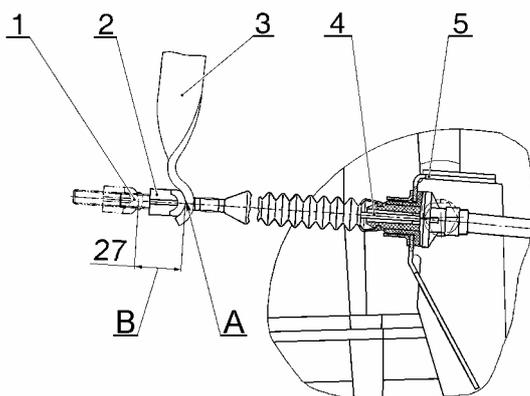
Механизм привода сцепления автомобиля ВАЗ-11183:
